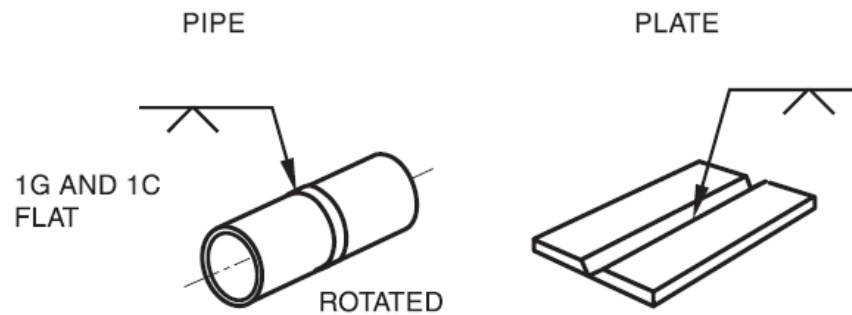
Posición de prueba 1C para soldadura de ranura, Cladding y Hardfacing (American Welding Society, 2009).
